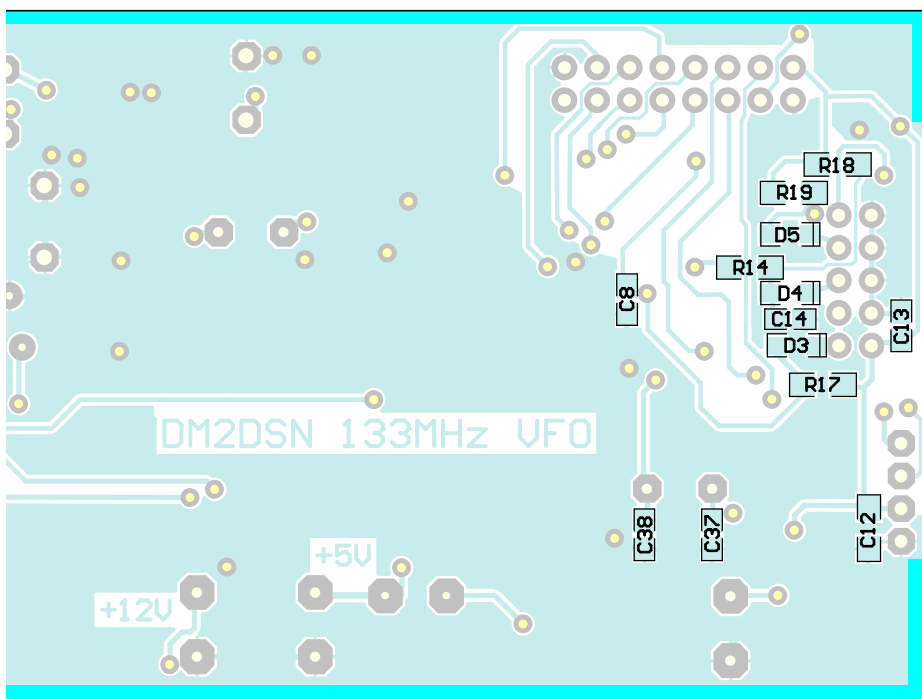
Einige Bauelemente sind auch auf der Lötseite zu bestücken.
